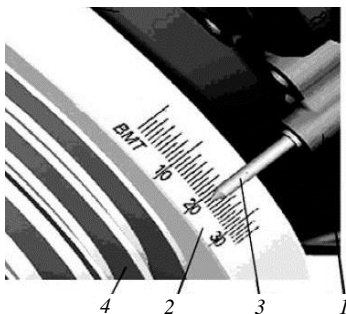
Установка угла опережения впрыска топлива двигателя Д-260:
